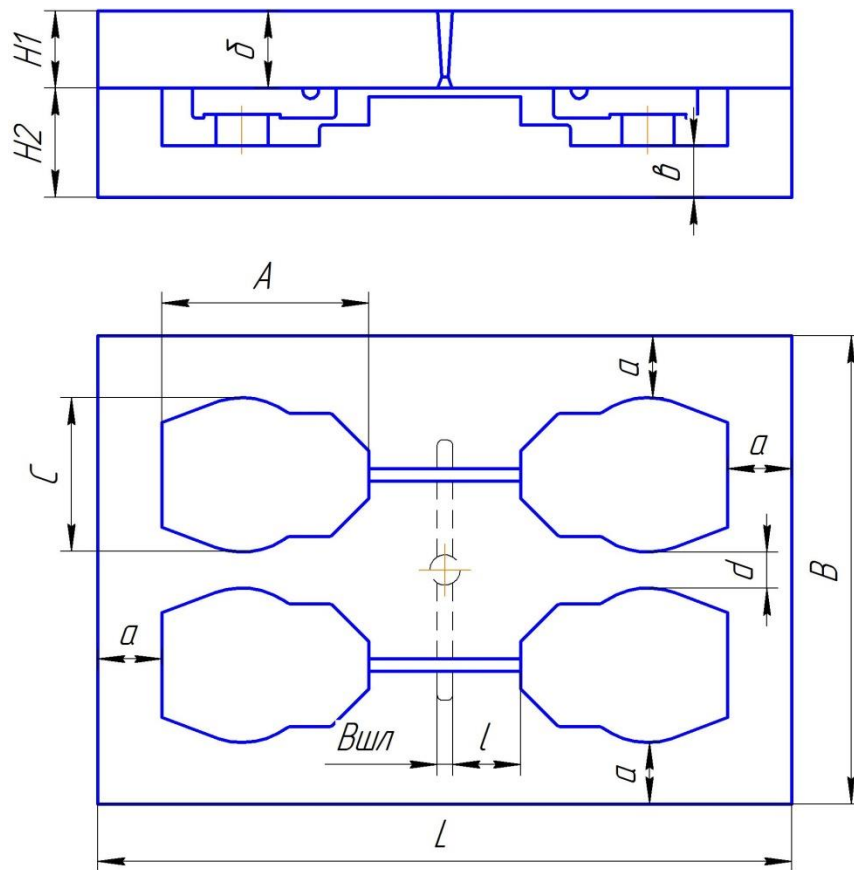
Розрахункова схема розташування виливків у формі
